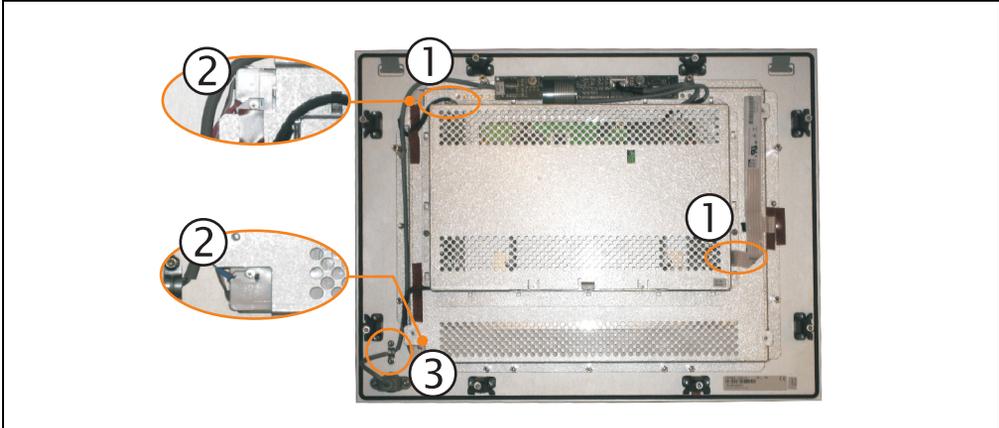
Automation Panel 15“ - Schrauben und Stecker lösen
